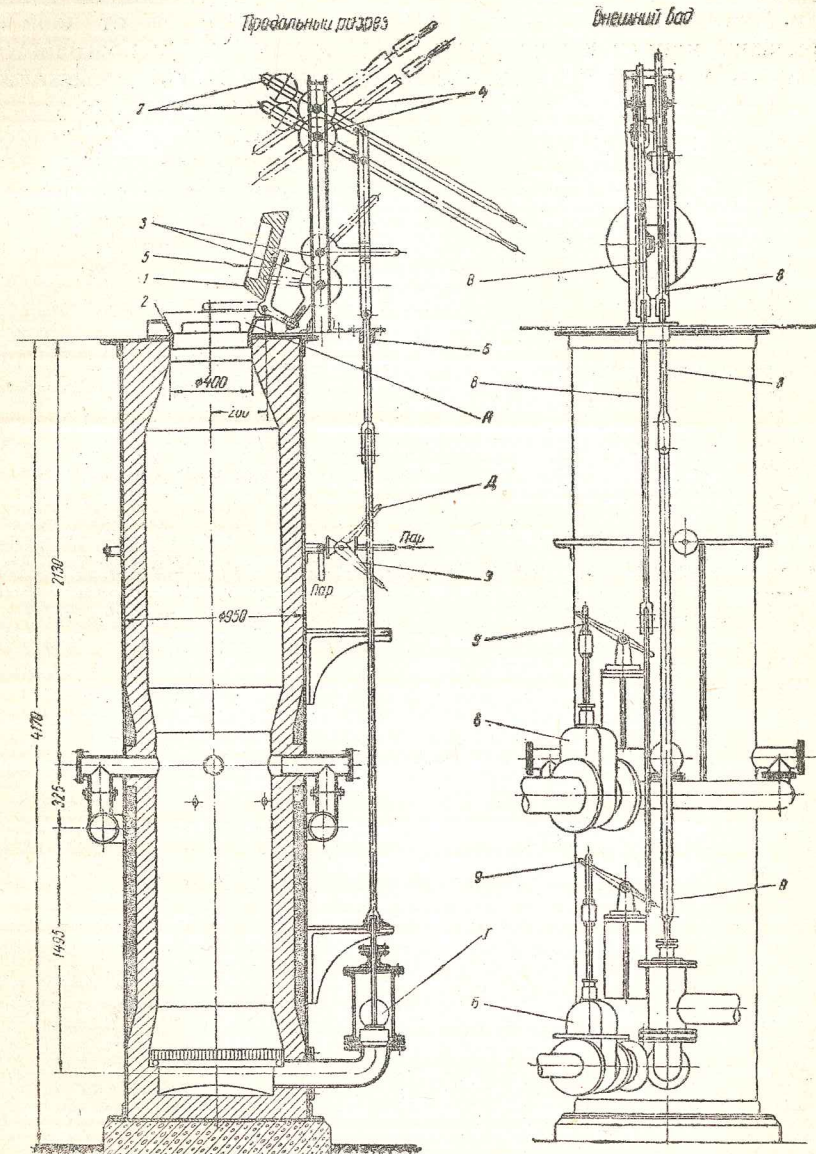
Газогенератор для получения водяного газа из местных топлив: А — загрузочный клапан; Б — клапан первичного воздуха; В — клапан вторичного воздуха; Г — газовый клапан; Д — паровой клапан; 1 — тарелка клапана; 2 — седло клапана; 3 — рычаги с зубчатыми секторами; 4 — запорные диски; 5 — угловой рычаг; 6 — направляющая плита; 7 — рычаги для управления; 8 — тяги; 9 — рычаги задвижек.
